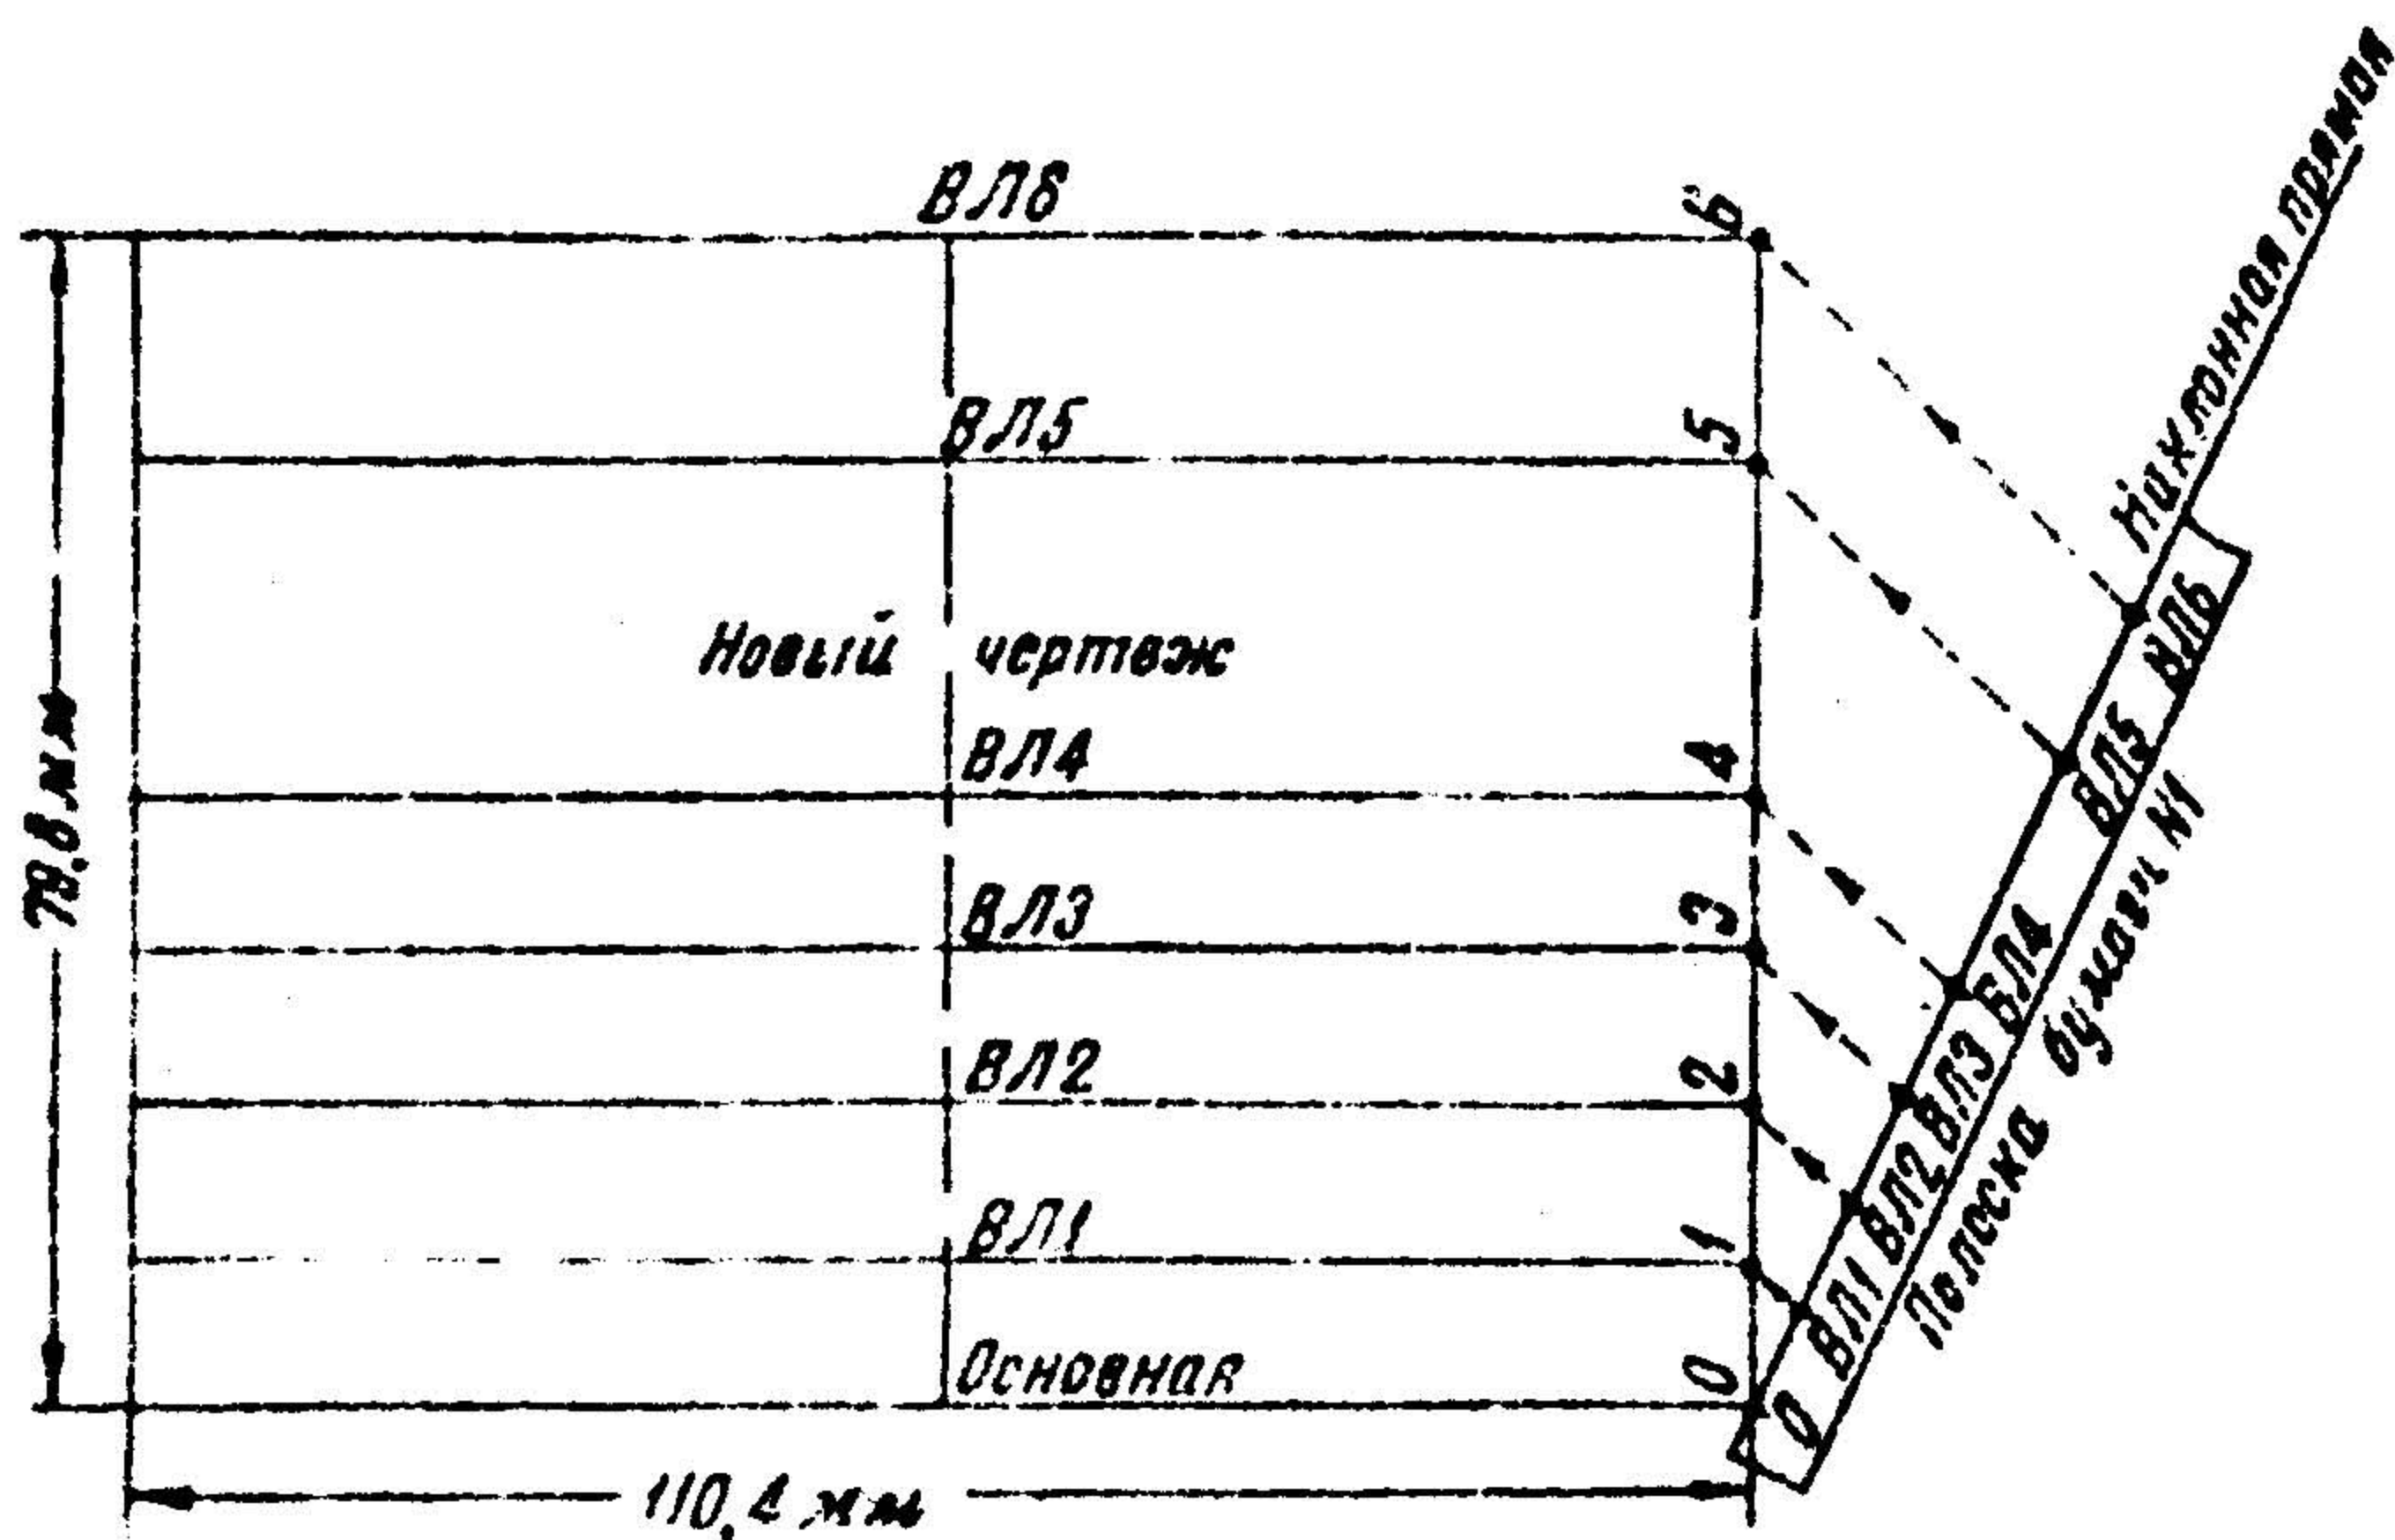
Прямоугольник для нового чертежа и перенесение на него разметки ватерлиний
